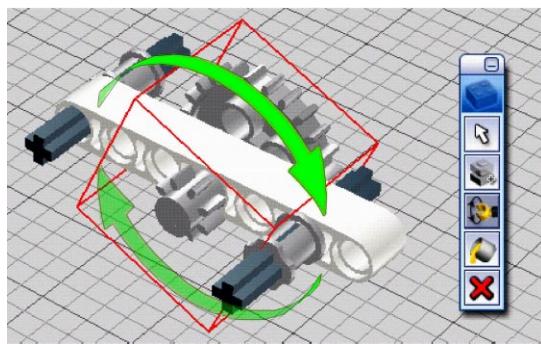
Поворот 24-зубой шестерни для последующейстыковки
